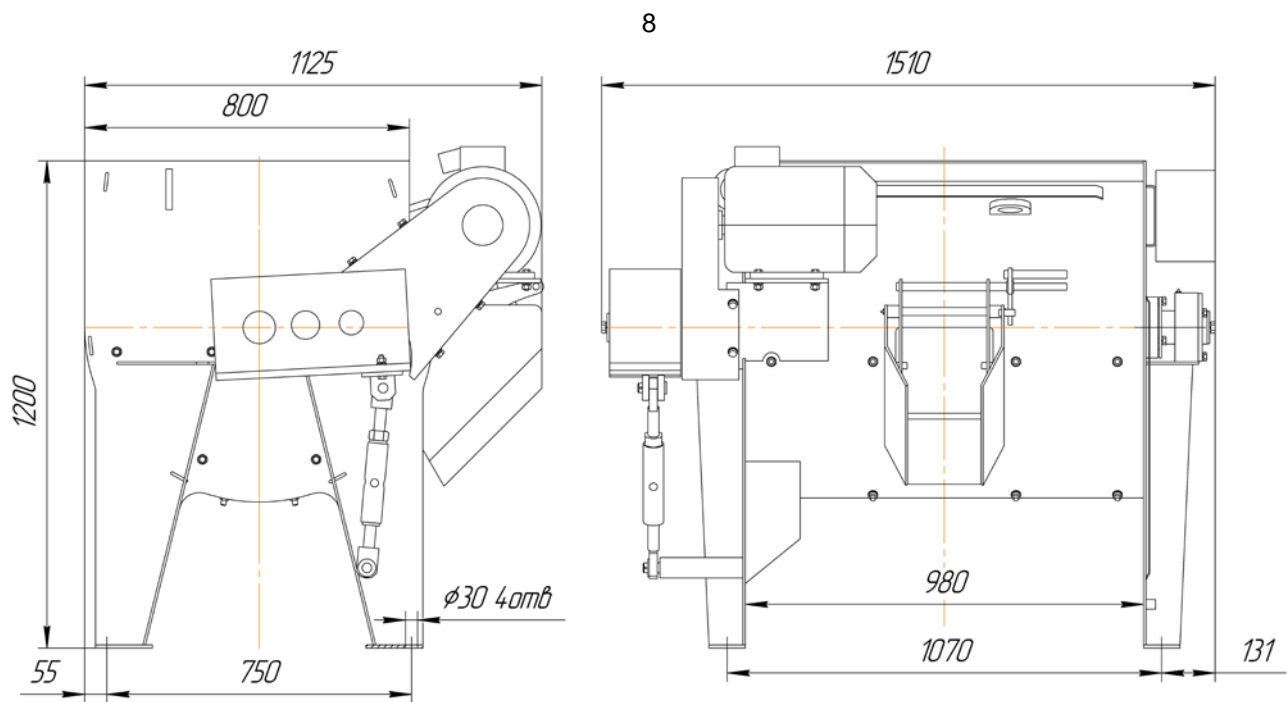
Габаритно-присоединительные размеры СГ-350.
